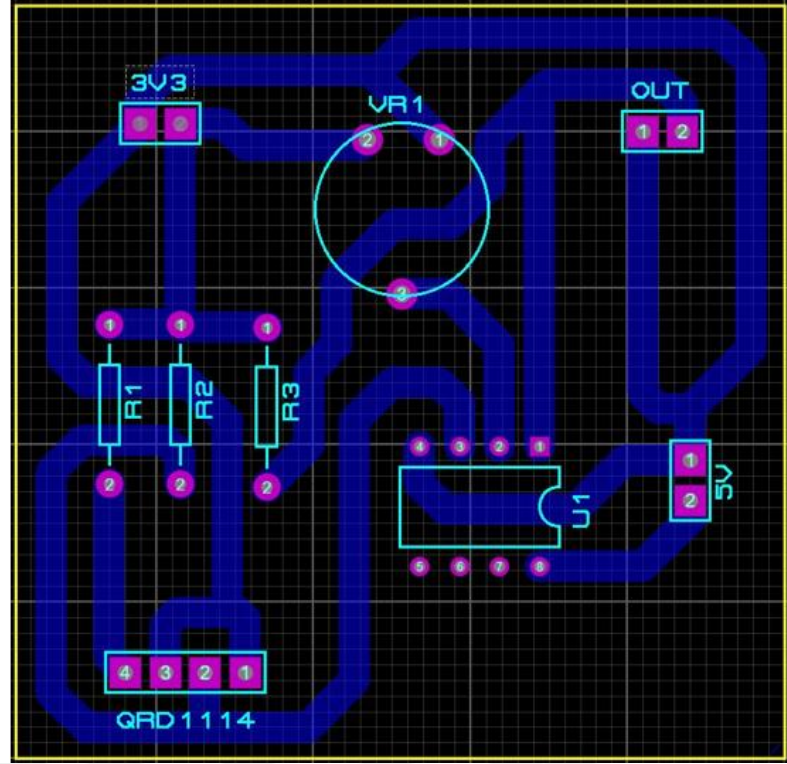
QRD1114 PCB ve şematik çizimleri.
